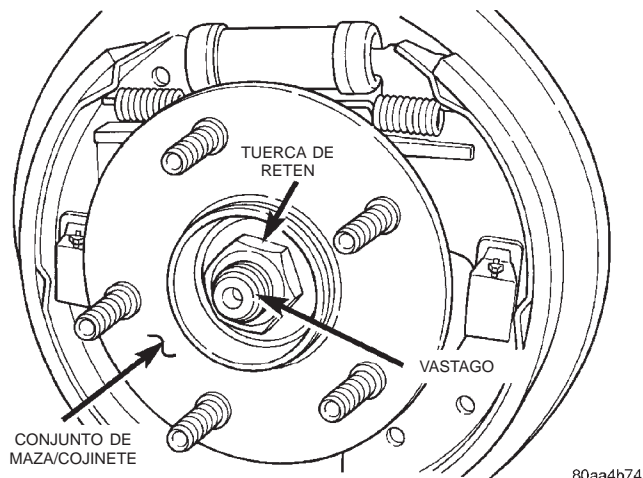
Tuerca de retén del conjunto de maza/cojinete trasero
